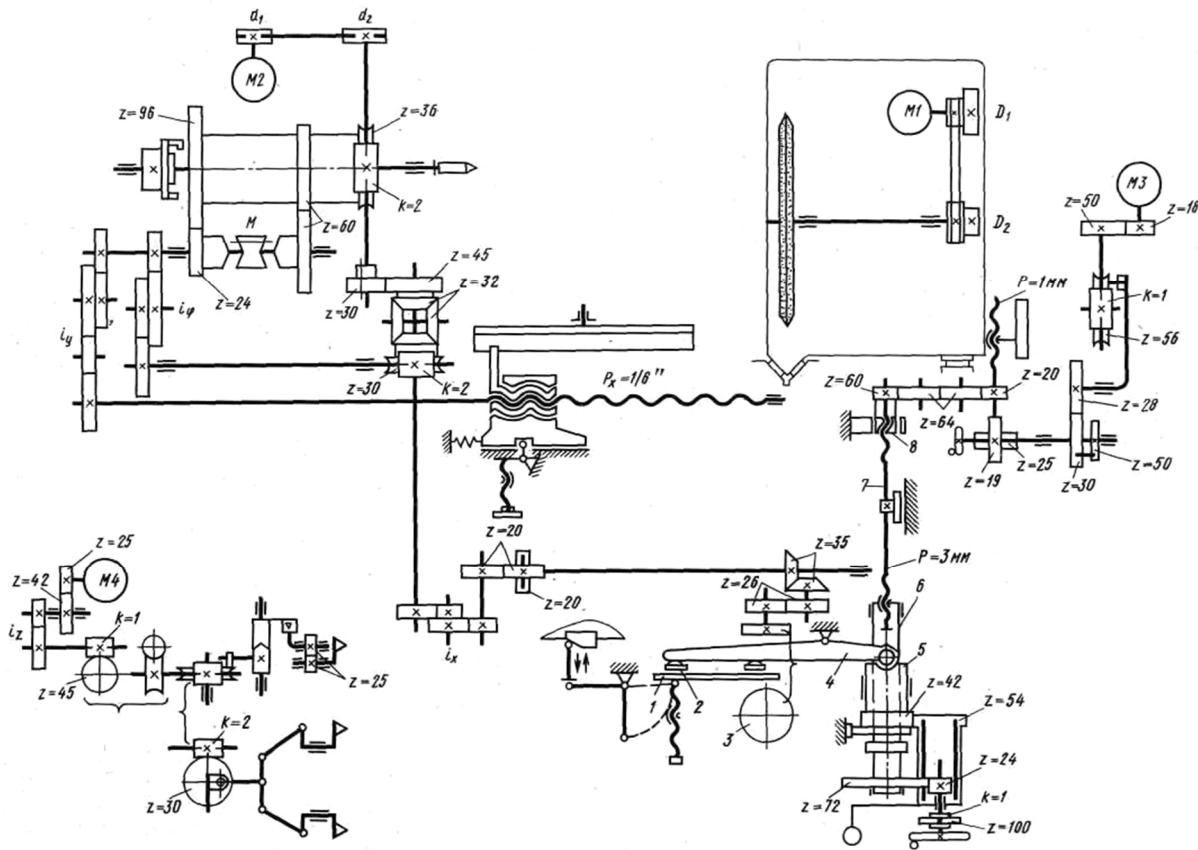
Кинематическая схема резьбошлифовального станка модели 5822М
